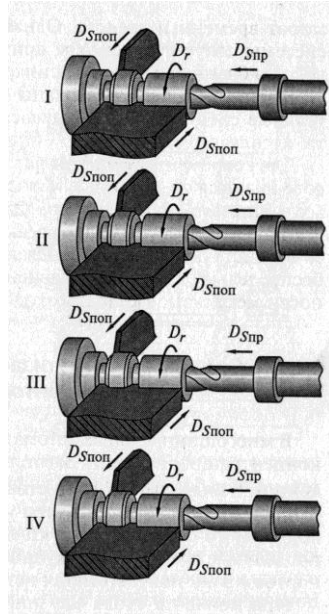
Схема роботи горизонтального багатшпindelного напівавтомата паралельної дії: I-IV- позиції одночасної обробки чотирьох заготовок.
